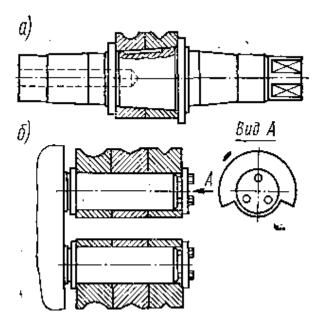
Схемы крепления вальцовочных бандажей (валков): а – резьбовым кольцом (на двуопорном вале); б – прижимной крышкой (на консольном вале)
